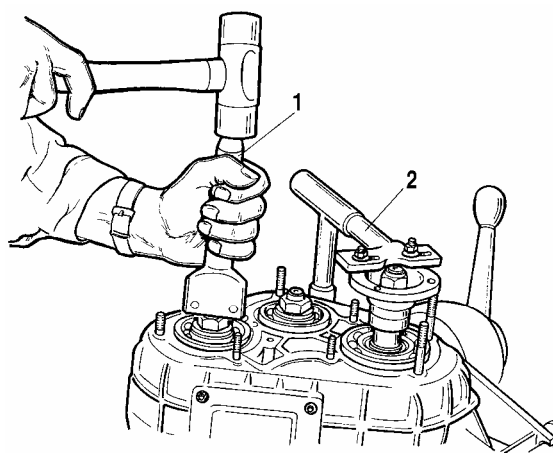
Обжатие гайки крепления фланца вала привода заднего моста:
